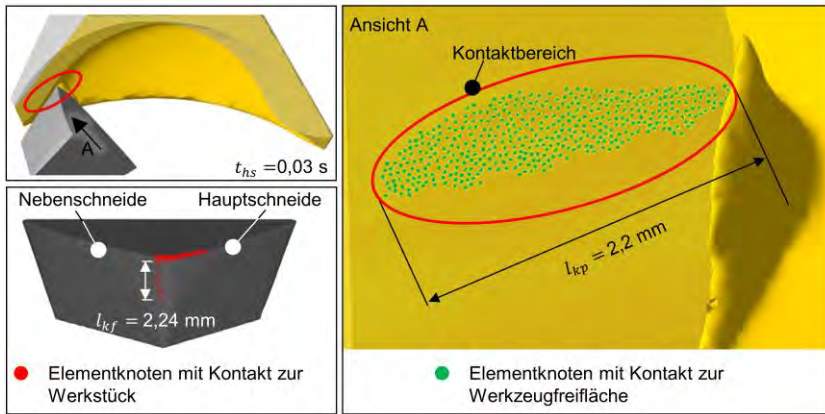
Freiflächenkontakt zwischen Werkzeug und Bohrungswand
